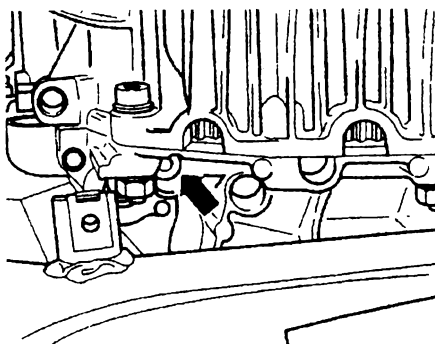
Местоположение пробки удаления охлаждающей жидкости из блока цилиндров шестицилиндрового двигателя
